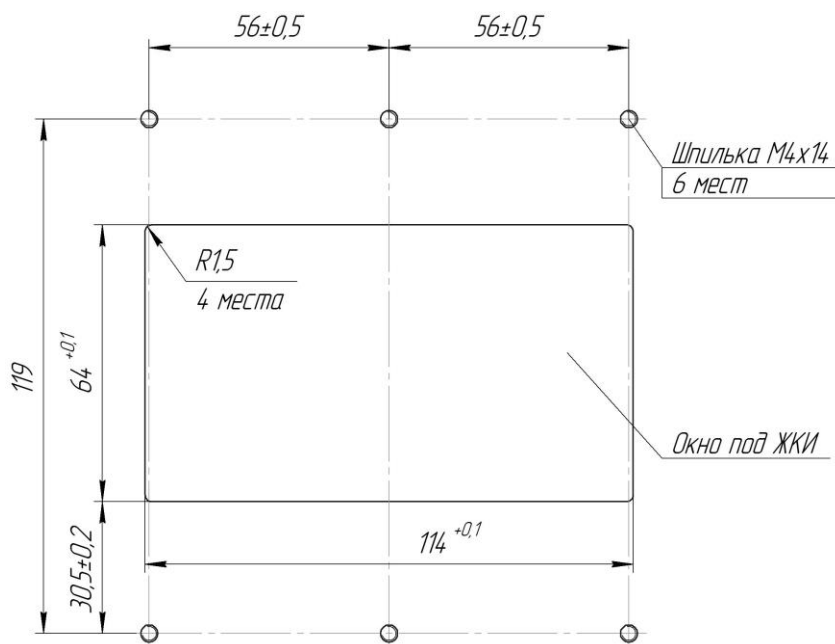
Разметка для крепления ЖКИ (вид со стороны установки ЖКИ)
